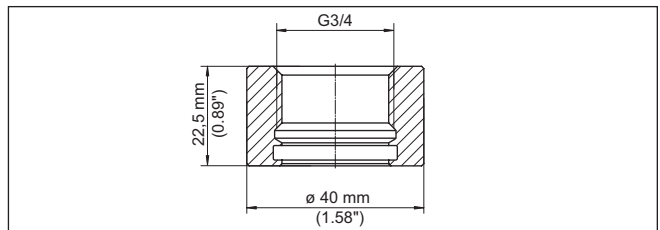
Dimensioni tronchetto a saldare filettatura G3/4 (ISO 228-1) - design igienico
